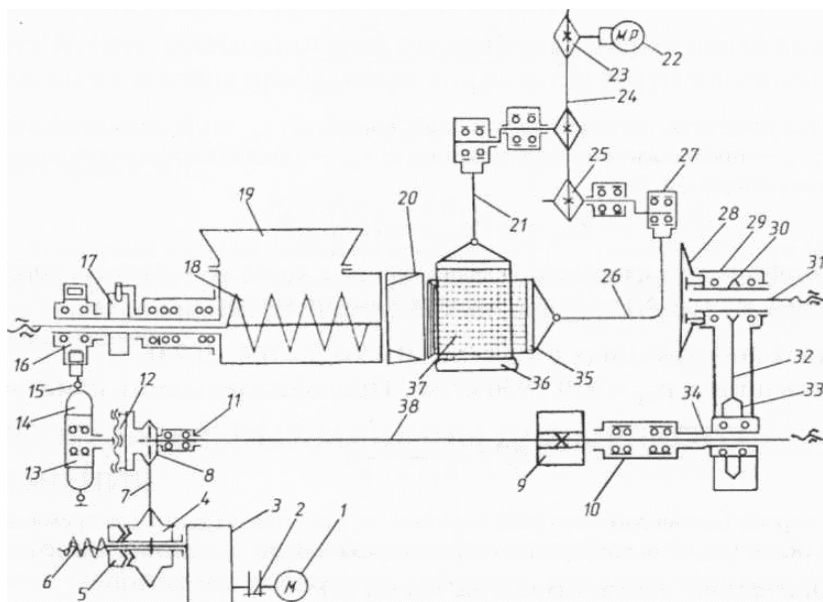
Кинематическая схема машины для резки шпика и мяса Я2-ФИА:
